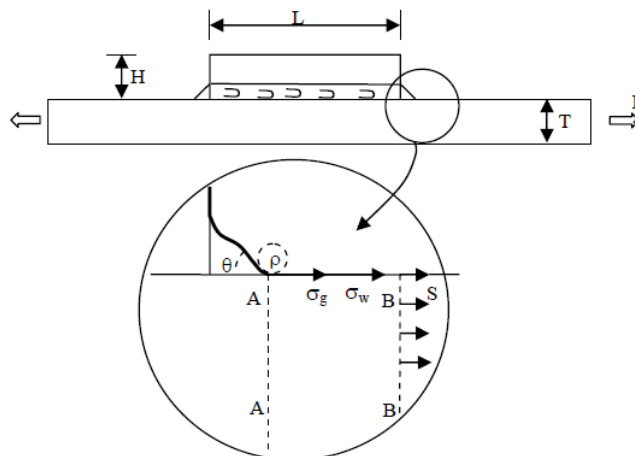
Definição de tipos de tensão em junta soldada (LASSEN e RECHO, 2006).
